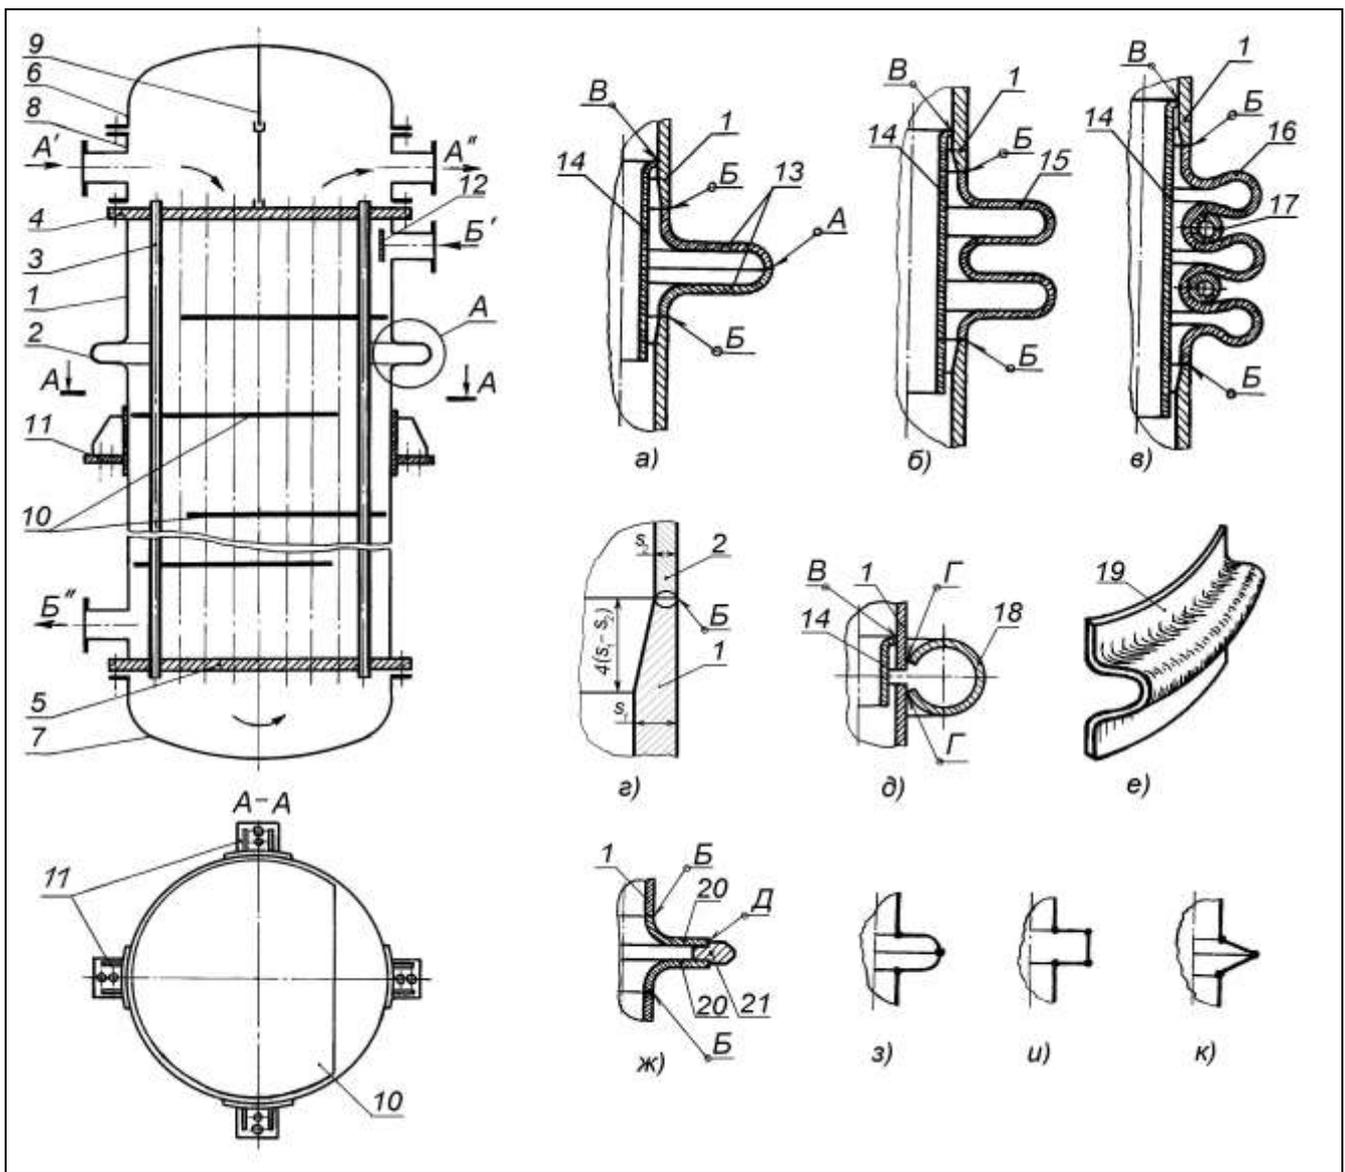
Теплообменник полужесткой конструкции типа К с различными видами компенсаторов 2 в корпусе 1: *а*) – с линзовым компенсатором из двух штампованных полулинз 13; *б*) – с цельным компенсатором из двух обкатанных волн 15; *в*) – с волнообразным компенсатором из трех волн 16; *г*) – схема подготовки кромок корпуса и компенсатора под стыковую сварку; *д*) – компенсатор из трубы 18; *е*) – секторный компенсатор 19; *ж*) – обкатанный компенсатор 20 с усиливающим кольцом 21; *з*), *и*), *к*) – сварные штампованные компенсаторы из листового материала
